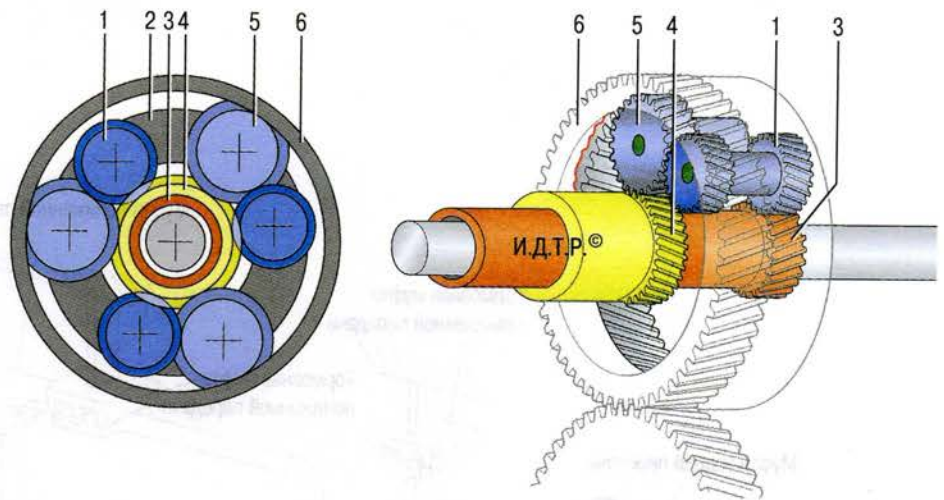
Планетарный редуктор системы Равинье: 1 – длинный сателлит; 2 – водило; 3 – малая солнечная шестерня; 4 – большая солнечная шестерня; 5 – короткий сателлит; 6 – коронная шестерня
